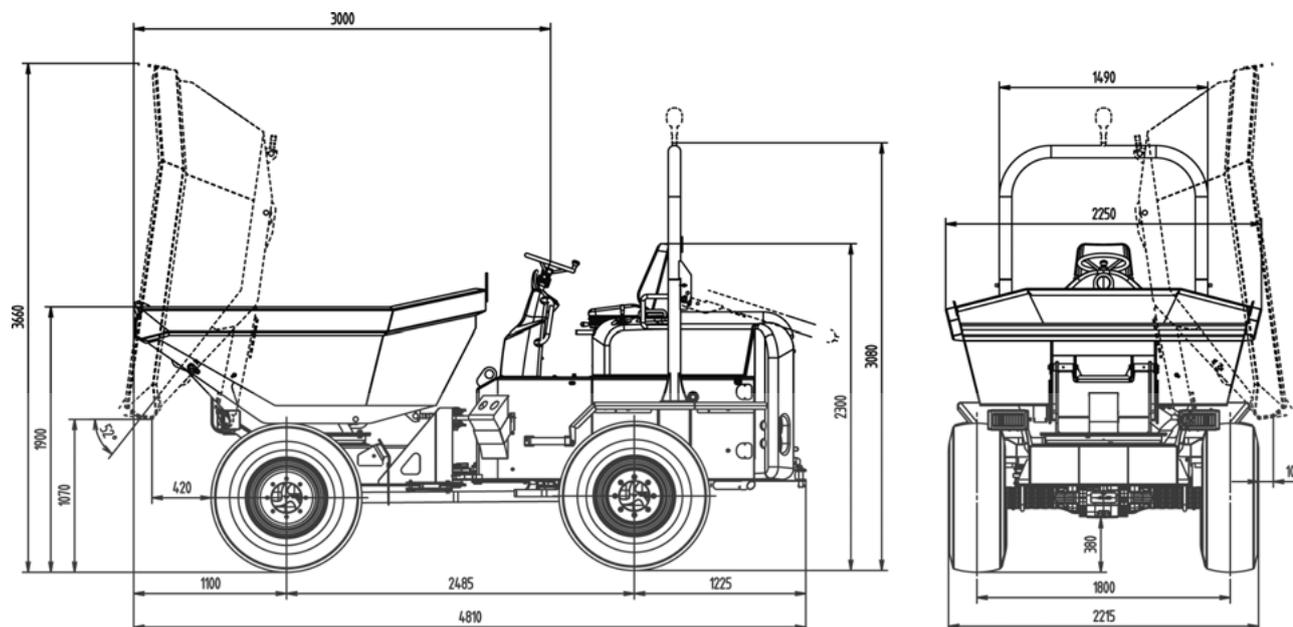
Dimensions de la machine (modèle 6001 Power)
